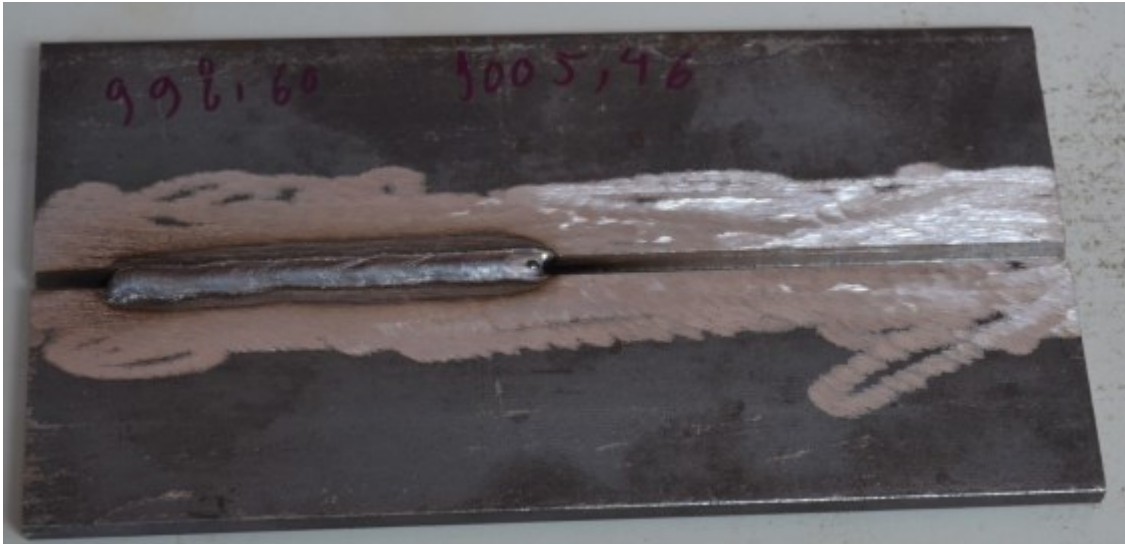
Solda realizada dentro do chanfro (GALVÃO, 2017)
